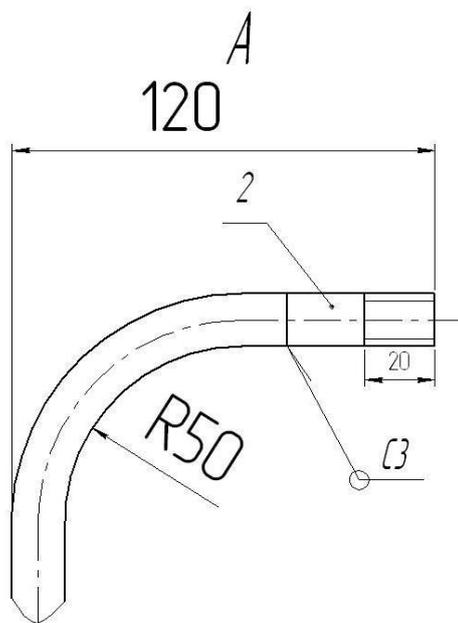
Схема водопровода внутриквартирного, вид А
